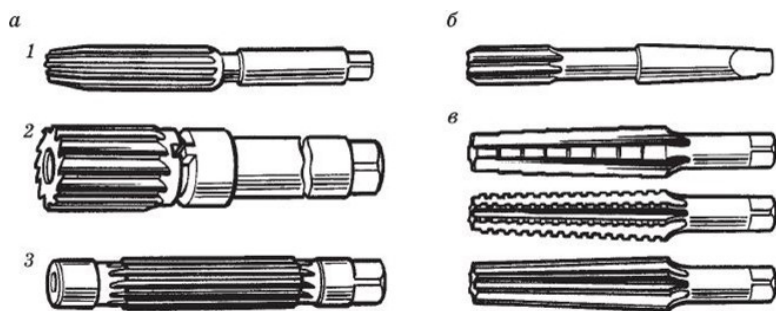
Типы разверток: а — цилиндрические ручные (1 — с прямым зубом; 2 — цилиндрическая насадная; 3 — регулируемая); б — машинная; в — комплект ручных конических разверток
